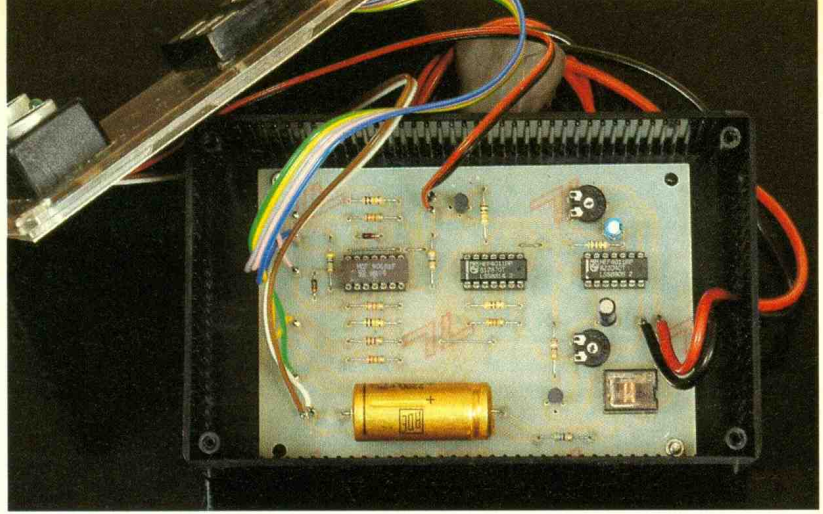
La carte imprimée épouse les dimensions du coffret.
